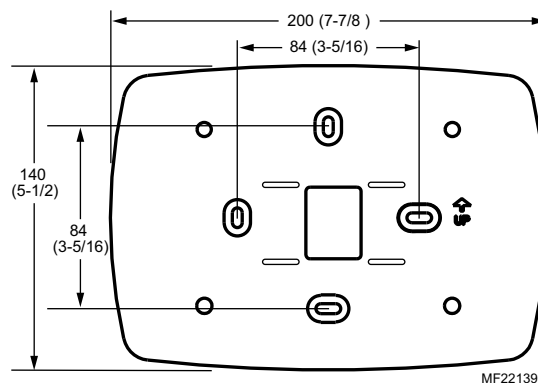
Encombrement de la plaque de recouvrement 32003796-001 en mm (po).
